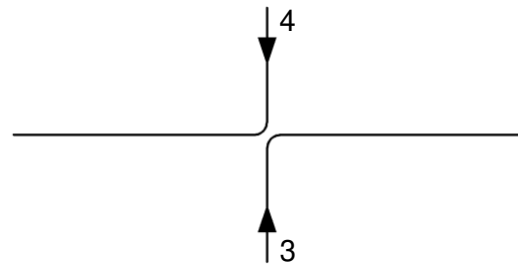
Schweißpfad Versuch 1 - Lage 2
